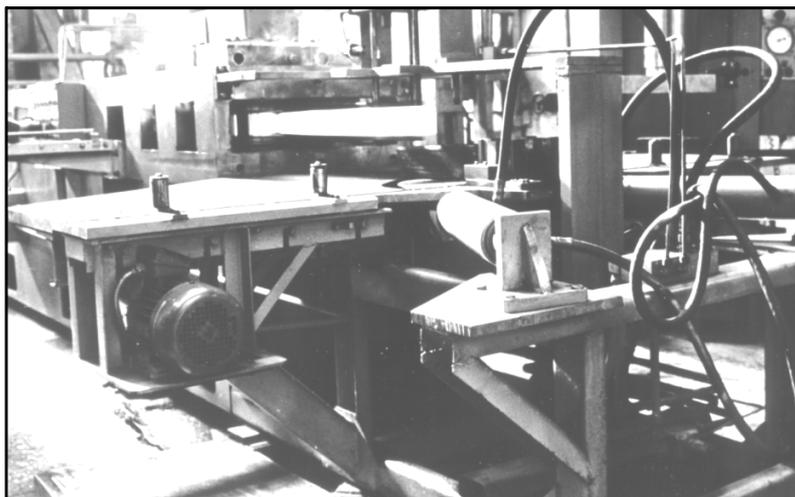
Прокатный стан в момент выхода двух прокатанных заготовок из клетки
